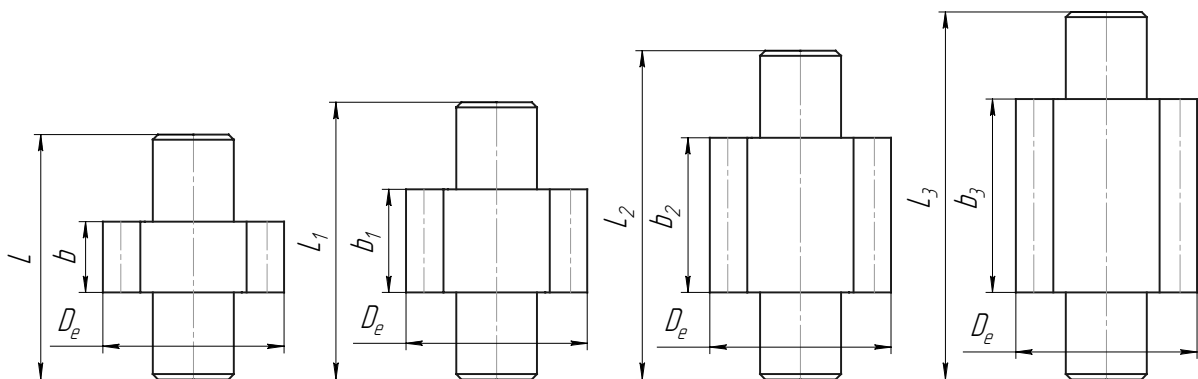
Эскизы шестерен одного типоразмерного ряда, отличающихся шириной венцов
